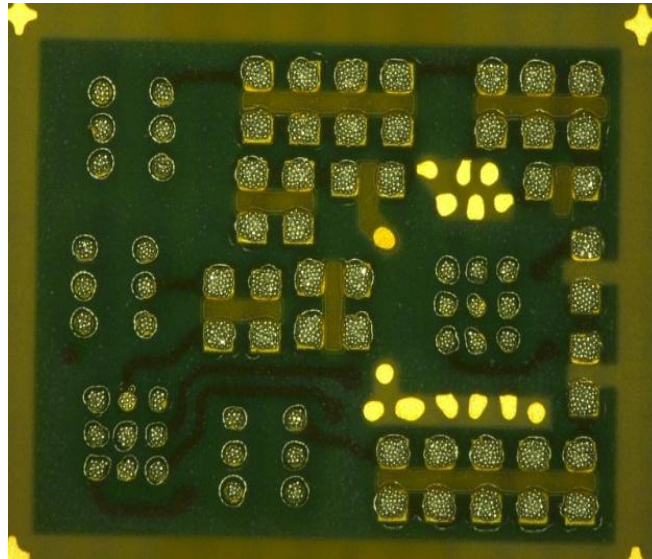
Impresión de soldadura de pasta a 105 micrones abertura cuadrada
